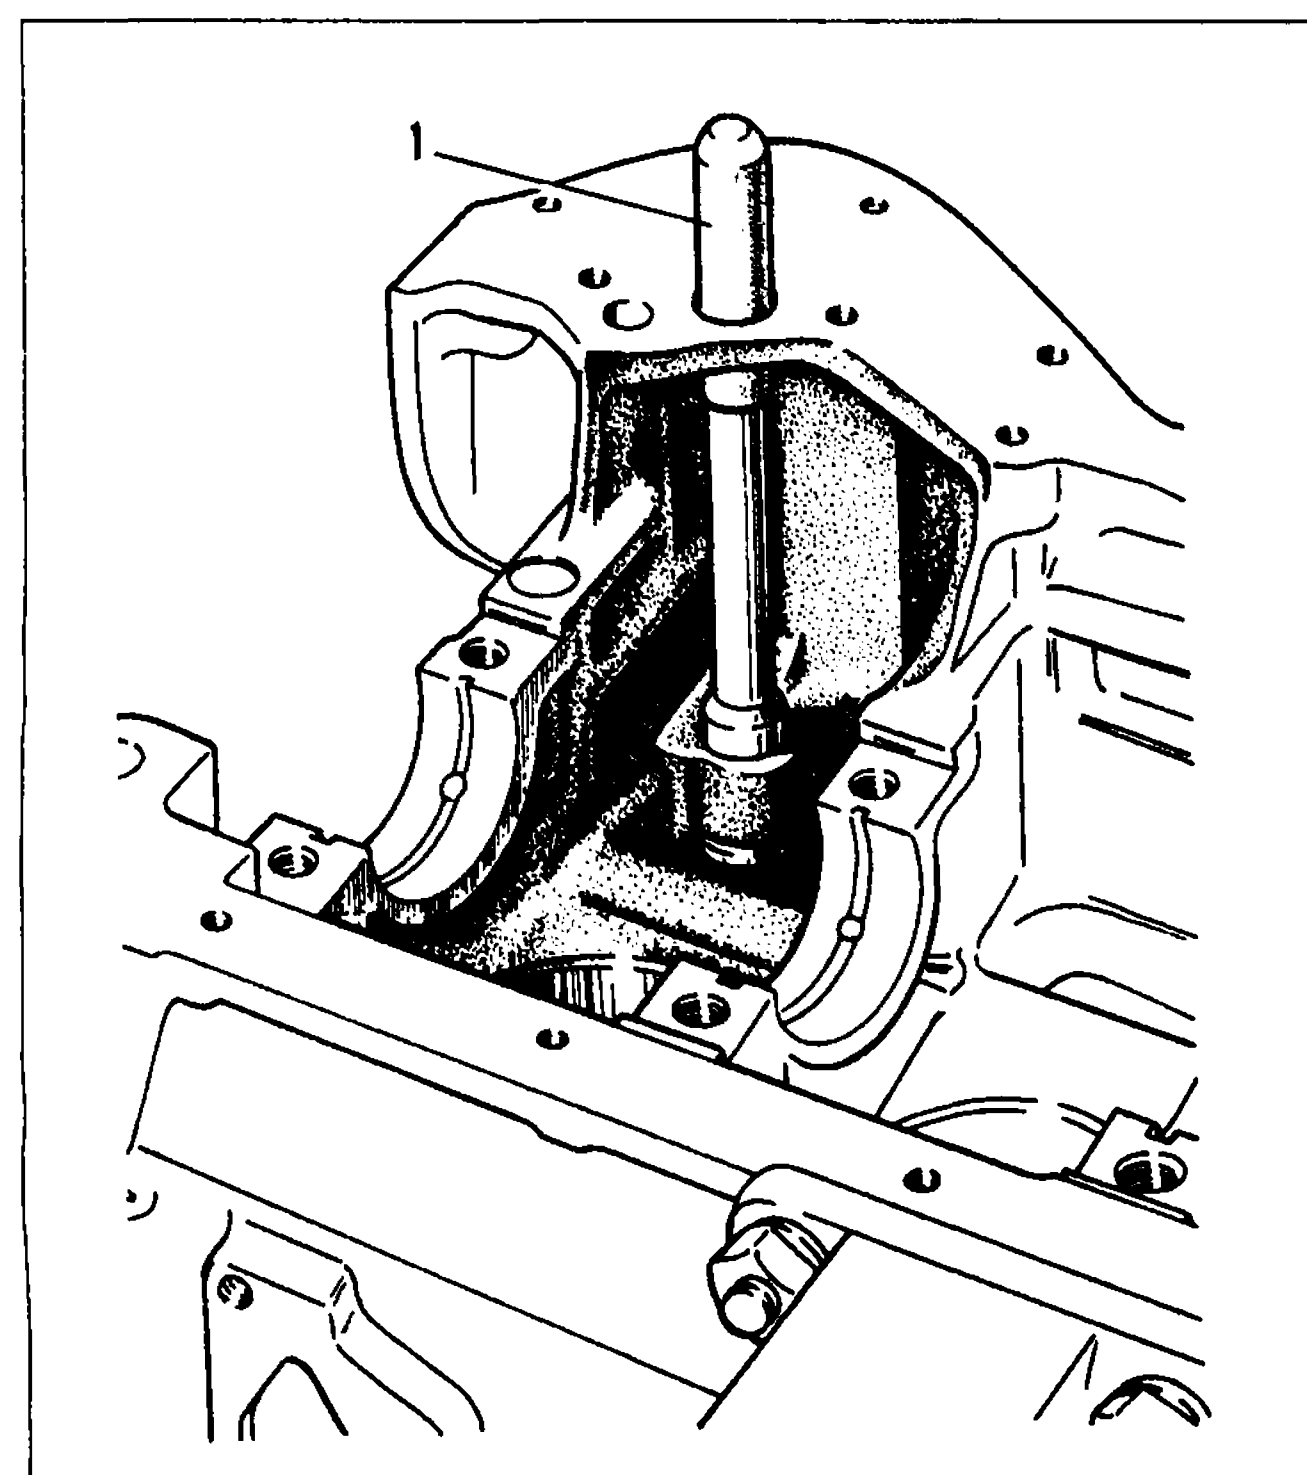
Выпрессовка втулки шестерни привода масляного насоса и распределителя зажигания:
